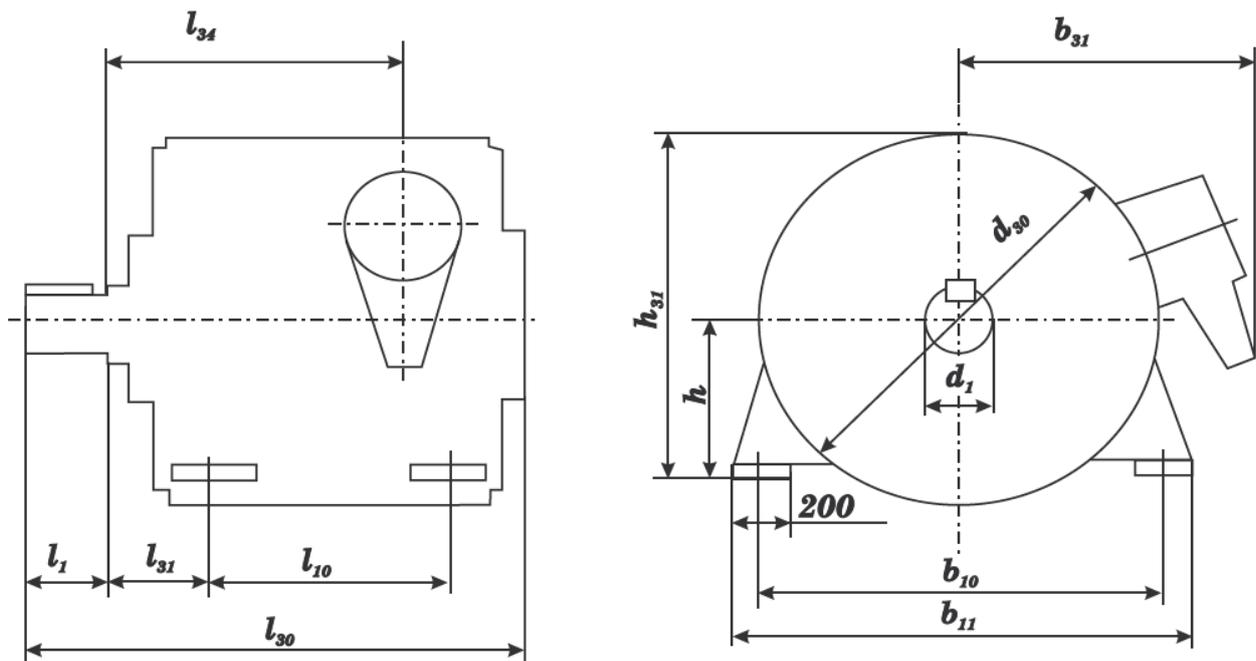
Габаритные, установочные, присоединительные размеры двигателей АН-2
